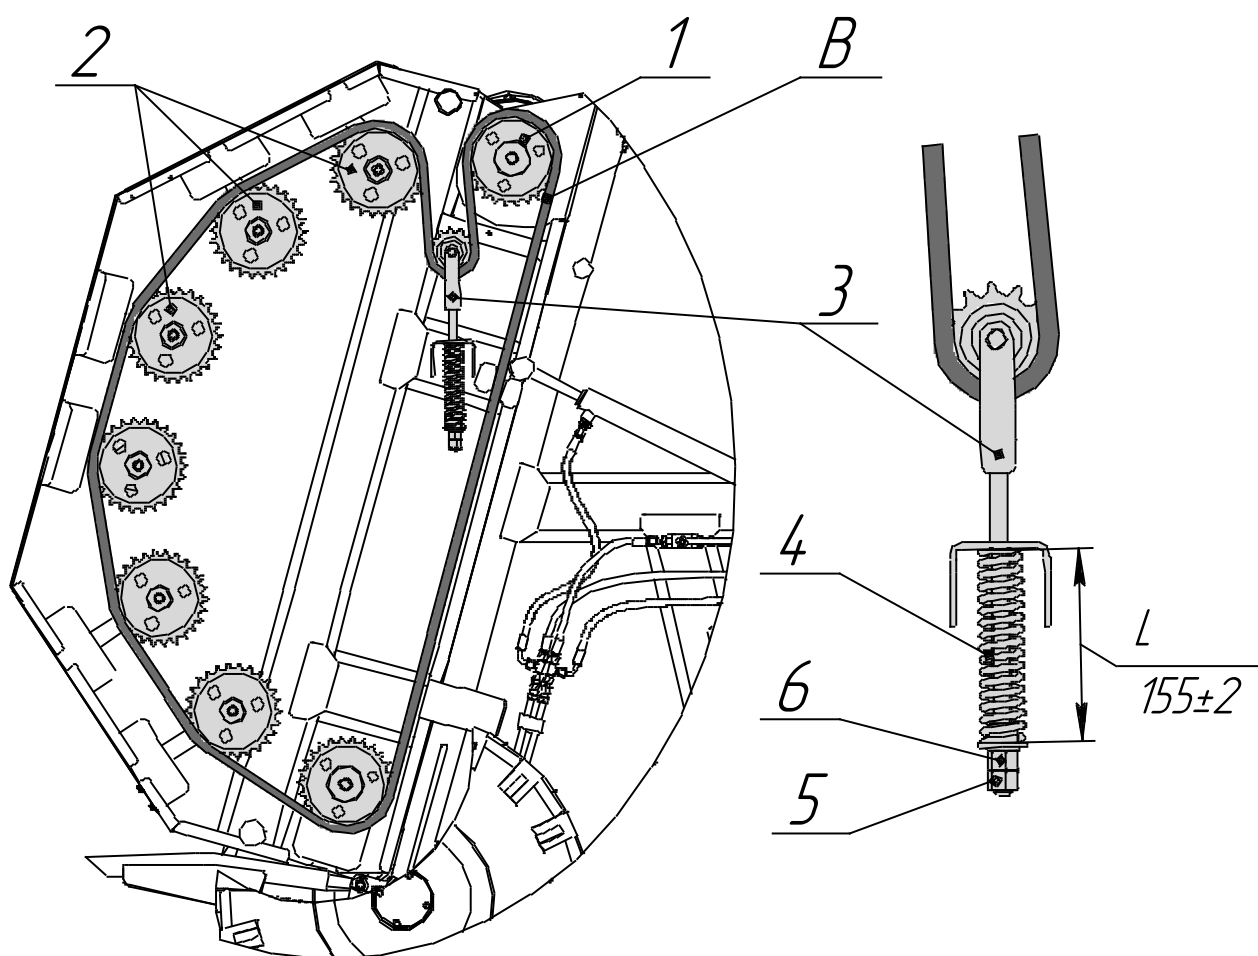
Регулировка натяжения цепи задней камеры: «В» - Привод правый; 1 – звездочка с вальцом привода цепи задней камеры; 2 – звездочки вальцов; 3 – натяжитель, 4 – пружина; 5 – контргайка; 6 – гайка.
